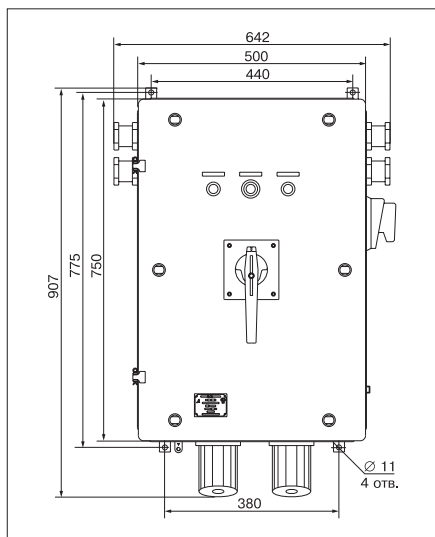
Габаритные и установочные размеры ящика ввода на токи до 63 А двухфидерного с двумя розетками и переключателем.
